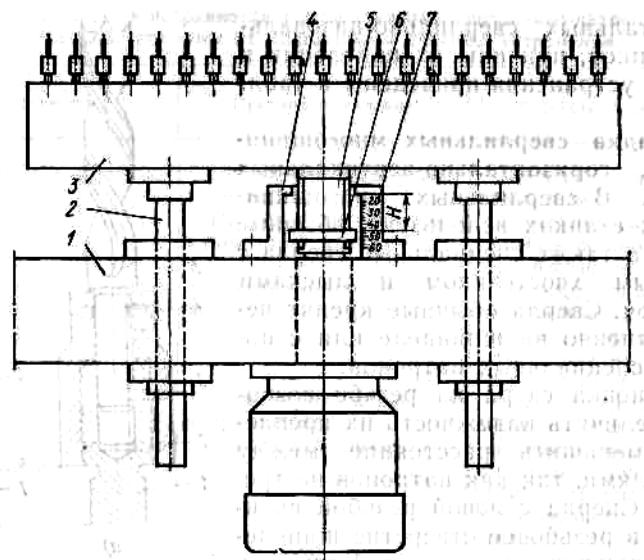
Настройка сверлильной насадки на глубину отверстий:
